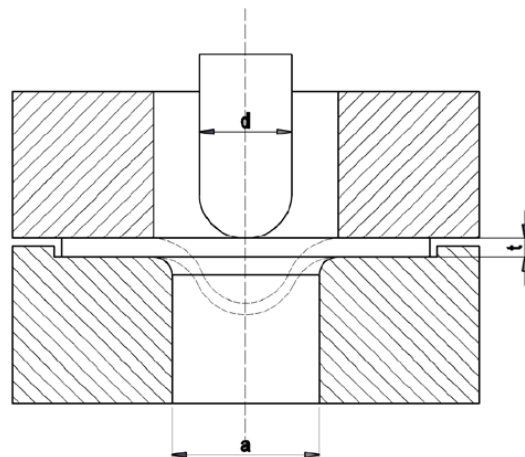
Corte transversal del dispositivo empleado para la realización de ensayos *Small Punch* [33]
